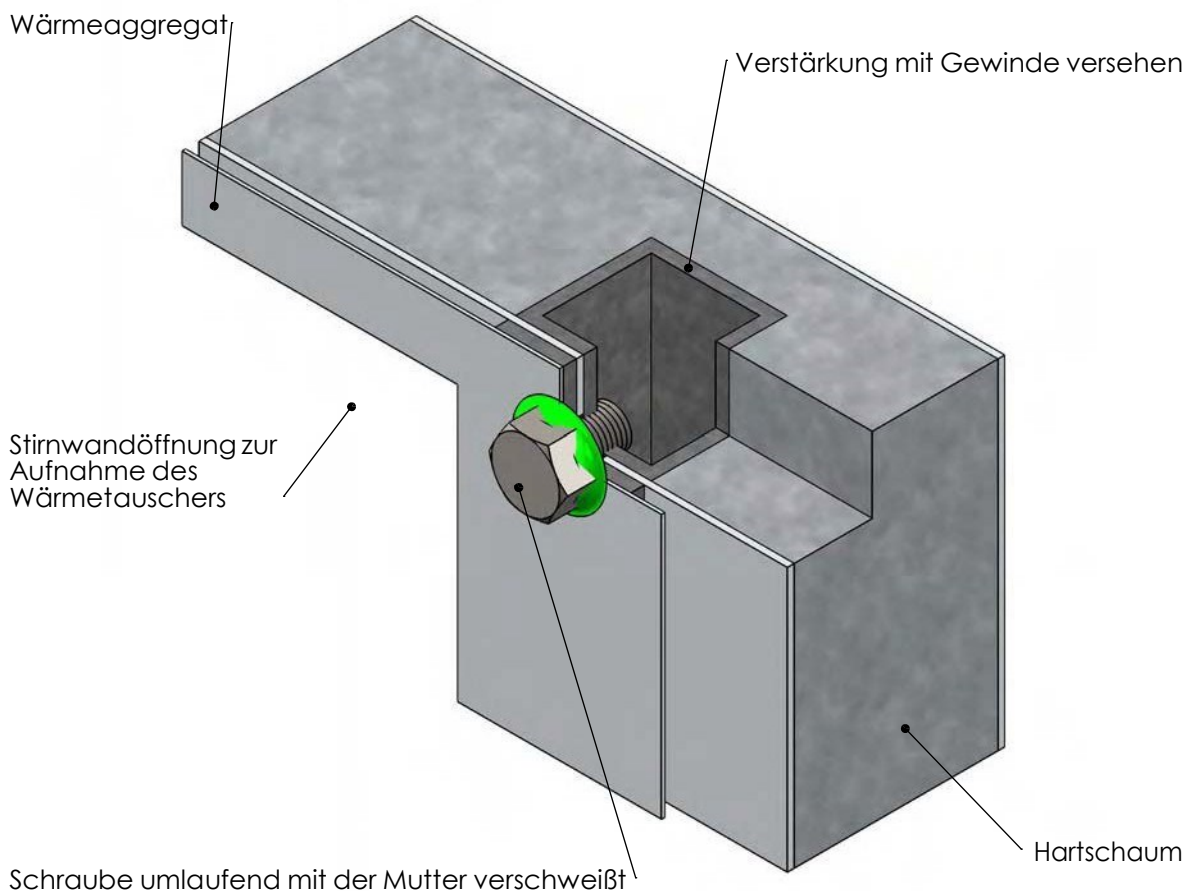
Sicherung mit außen verschweißten Schrauben
